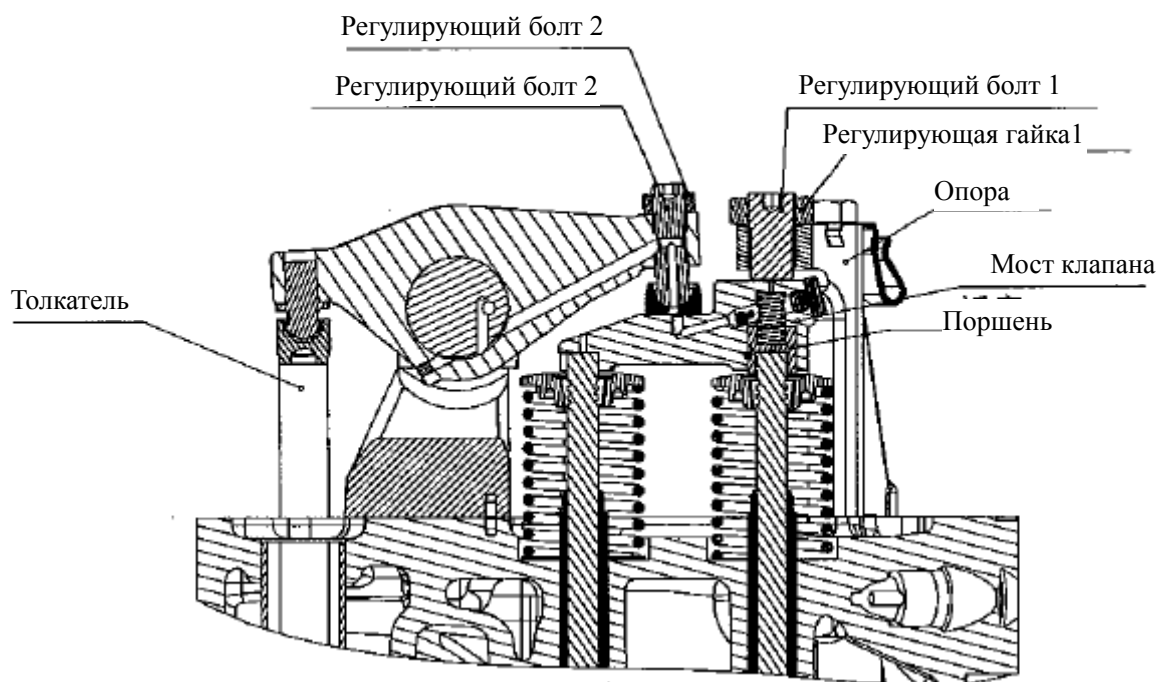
Выпускной клапан и регулировка зазора EVB
